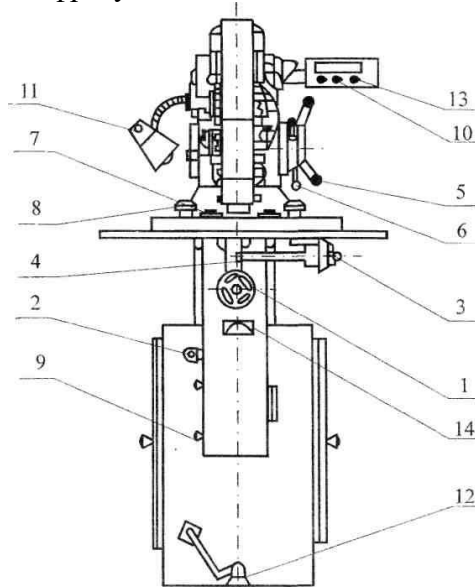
Загальний вигляд верстата ВФК-2: 1 - маховичок переміщення стола; 2 - рукоятка фіксування супорта стола; 3 - рукоятка управління копійвальним пальцем; 4 - кнопка затискання копійвального пальця; 5 - рукоятка повороту револьверної головки з упорами; 6 - гвинти упорів револьверної головки; 7 - кнопка кріплення кутника до стола; 8 - кнопка кріплення накладки до кутника; 9 - гвинти регулювання притискних планок; 10 - кнопки умикання і вимикання головного приводу; 11 - тумблер умикання місцевого освітлення; 12 - педаль управління підйомом і опусканням головки фрезувальної; 13 - лампа сигнальна; 14 - вказівник підйому та опускання стола
